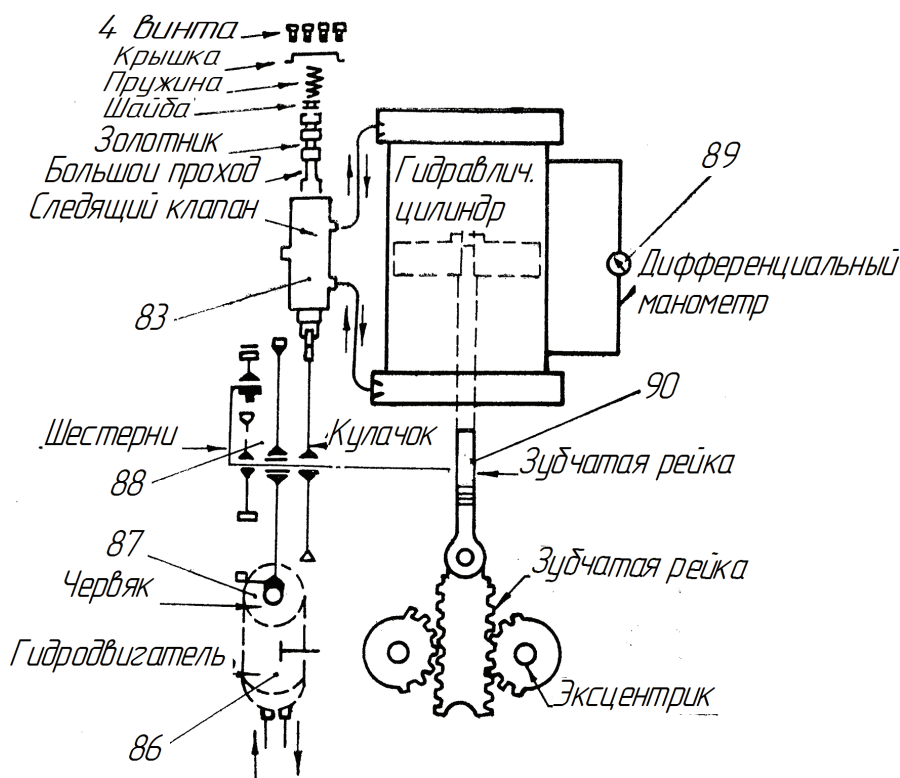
Кинематическая схема гидрораспределителя автоматической регулировки валков
